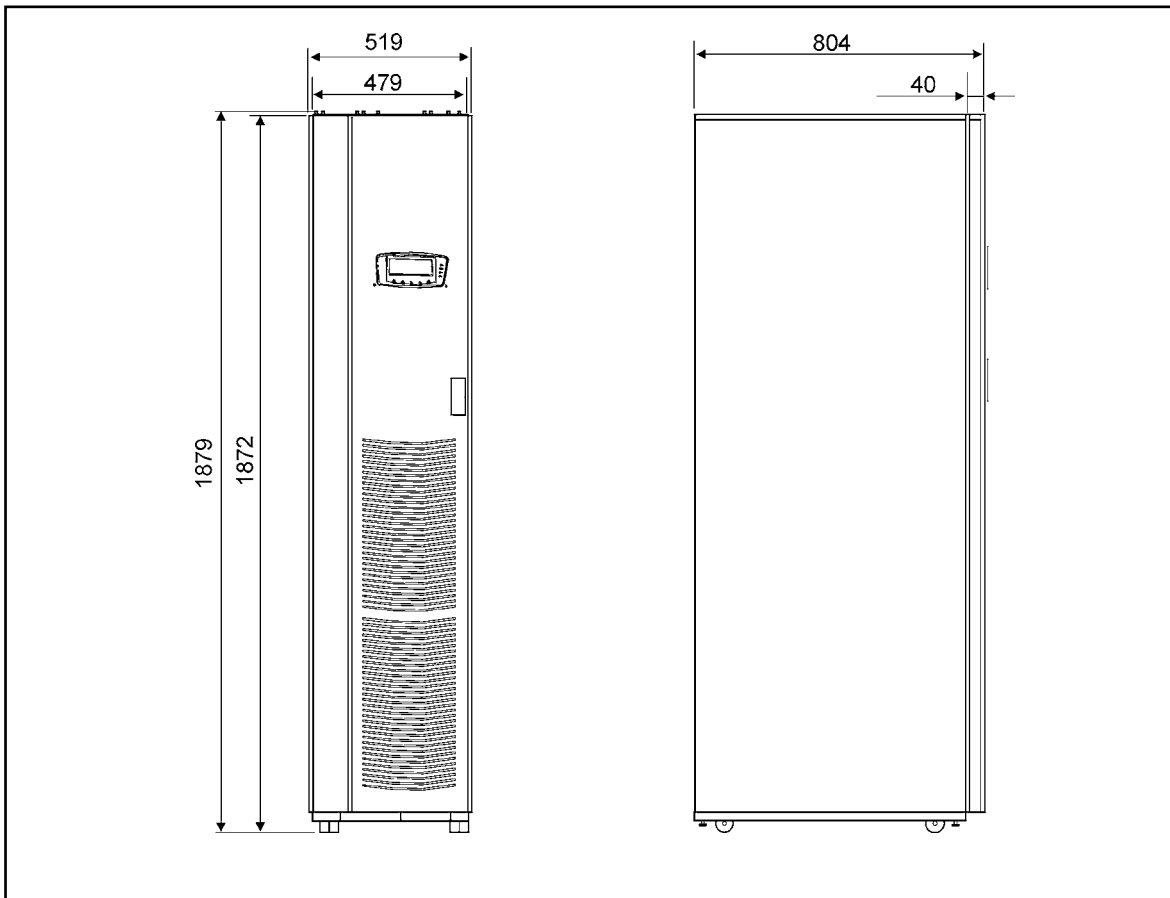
Abmessungen – USV-Schrank (40-80 kVA)
